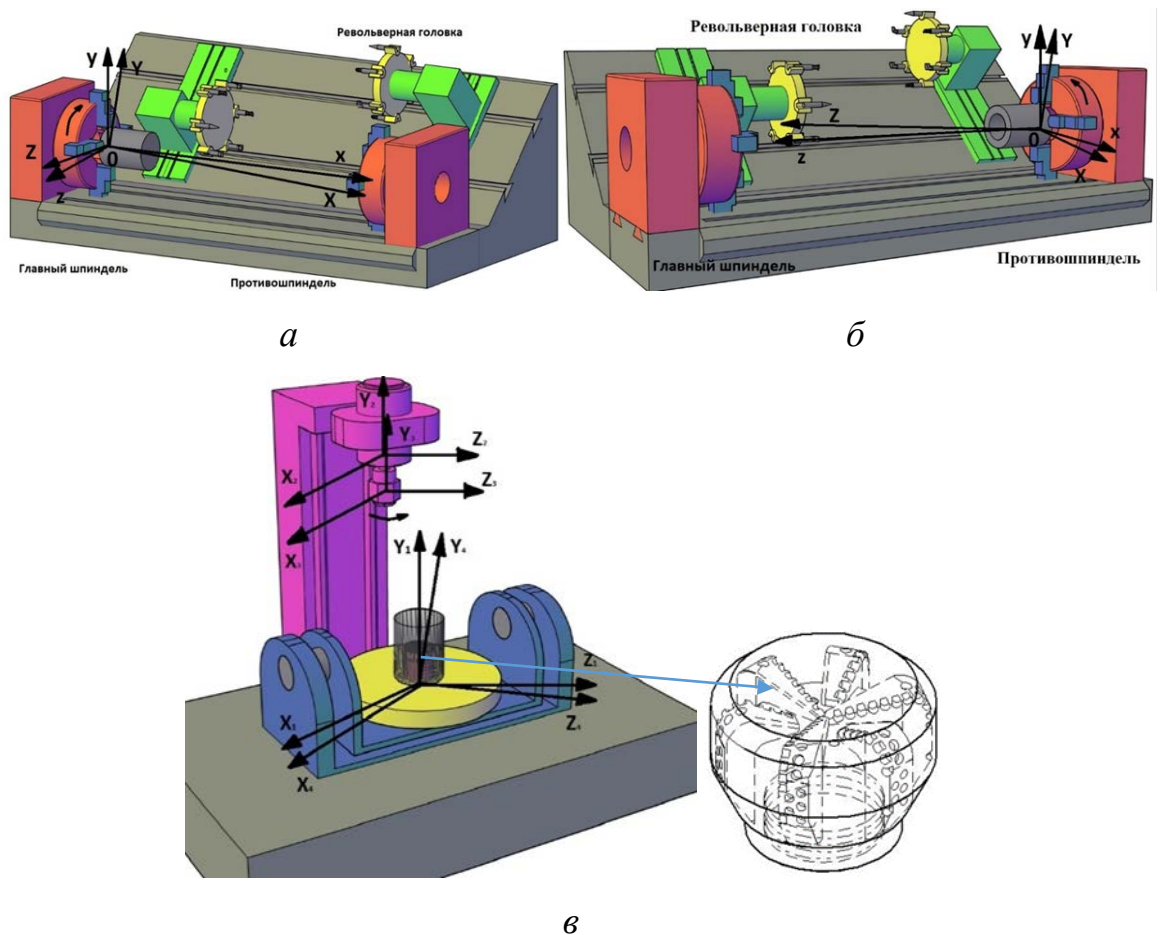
Координатные системы станка, детали и инструмента: а – установ А токарной операции (главный шпиндель); б – установ Б токарной операции (противошпиндель); в – фрезерная операция на специальной резьбовой оправке
